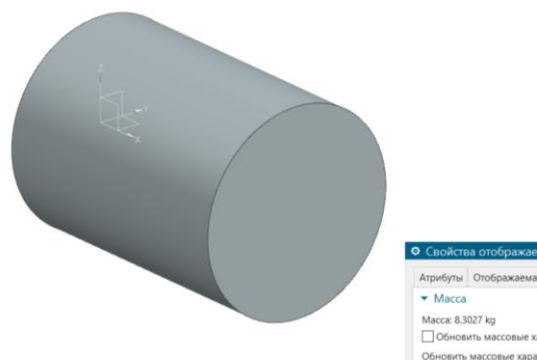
Модель заготовки, що отримується з прокату
